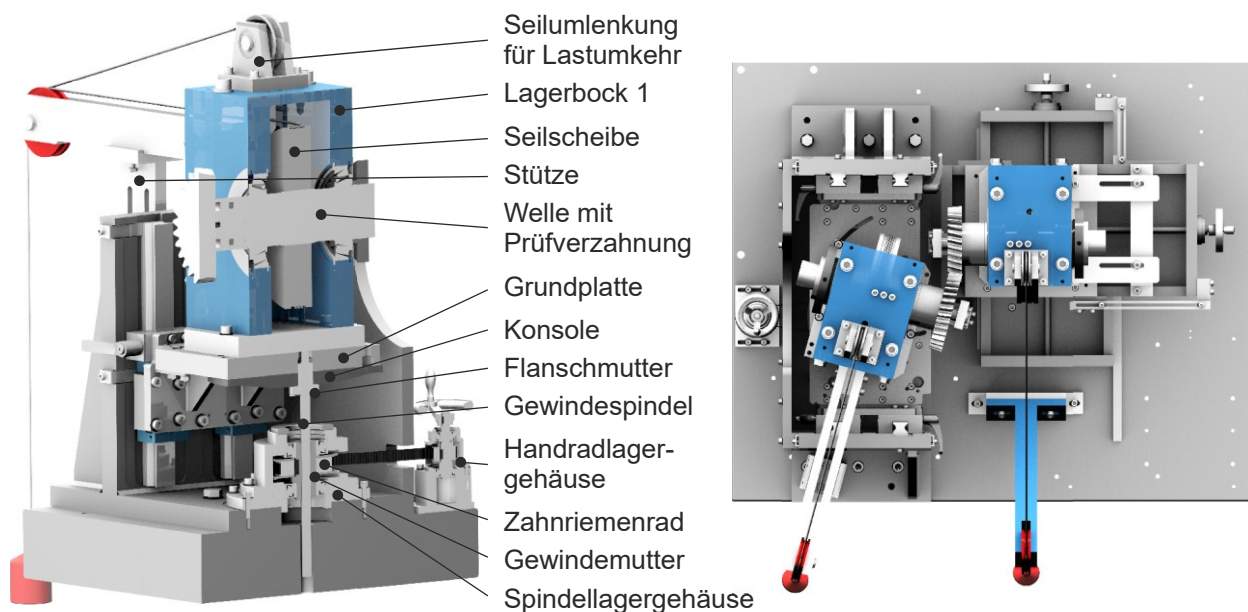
Schnittansicht Hubmechanismus (links, Schnittebenen durch Spindelachse und Zahnrad) [SCHÖLER19B] und Draufsicht DÜP (rechts)
